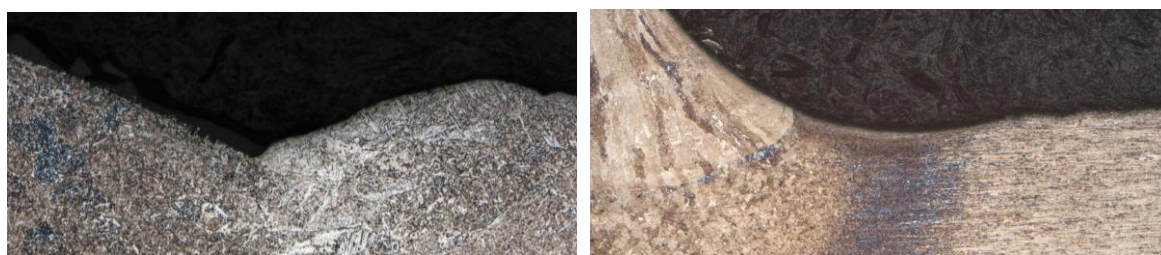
Zkušební vzorek s příčným svarem X (identicky pro svar V)Fig. 19: Specimen with transverse butt X-weld (identical for V-weld)
